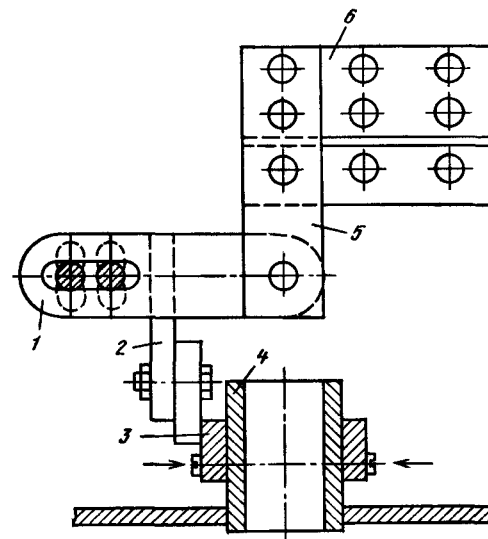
Крепление фиксирующего приспособления по выдвижной линейке стенда:
